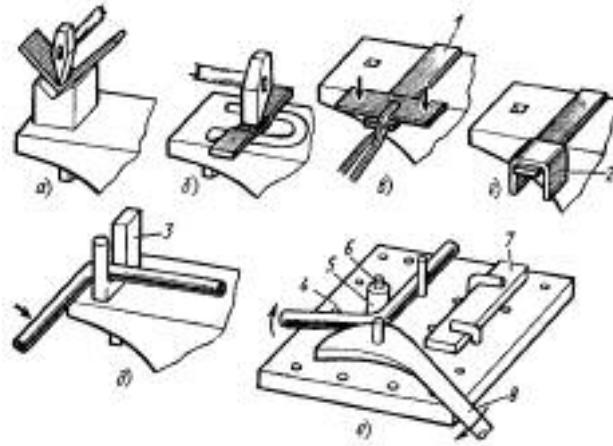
Способыгибки заготовок с применением приспособлений
